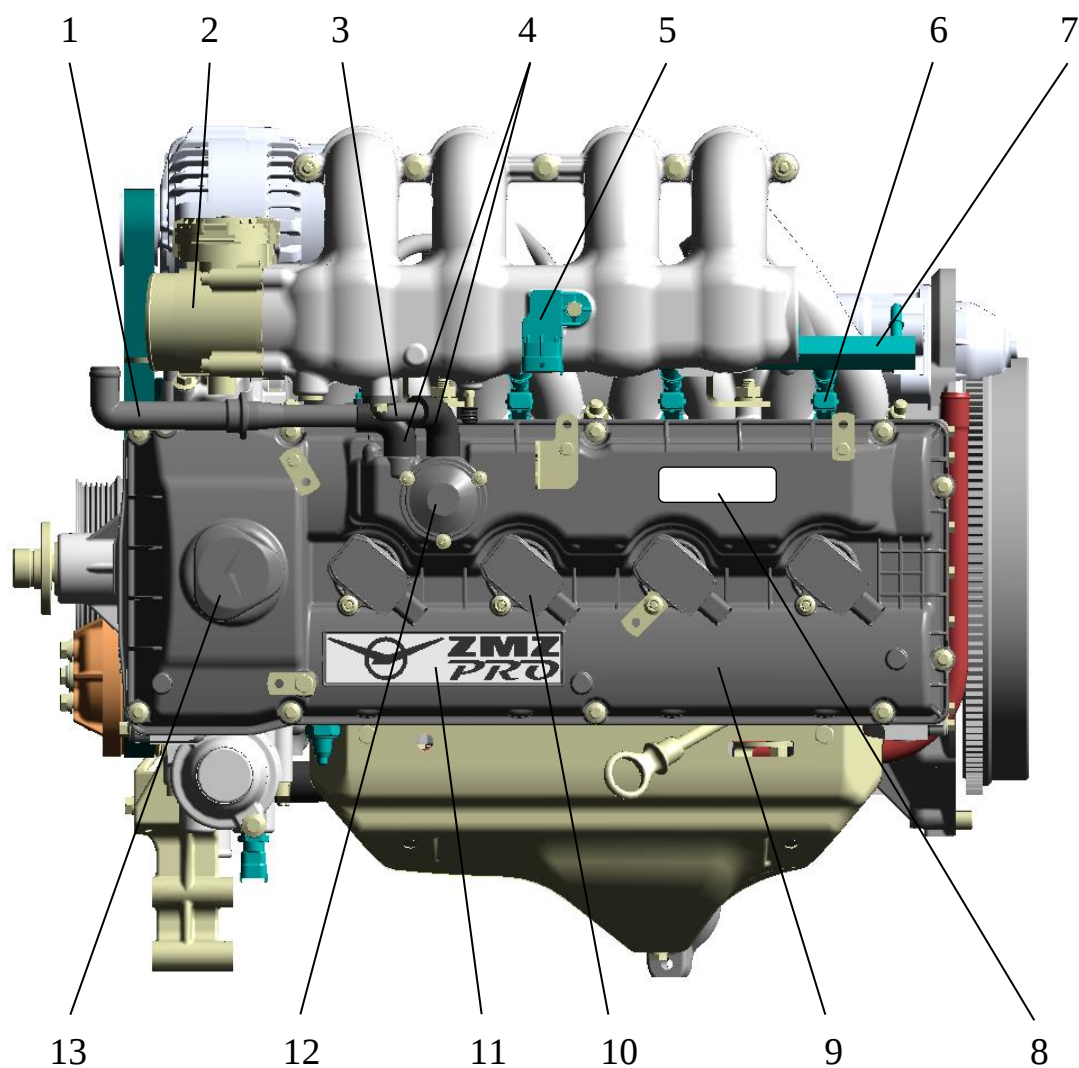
Вид двигателя ЗМЗ-409051.10 сверху:
